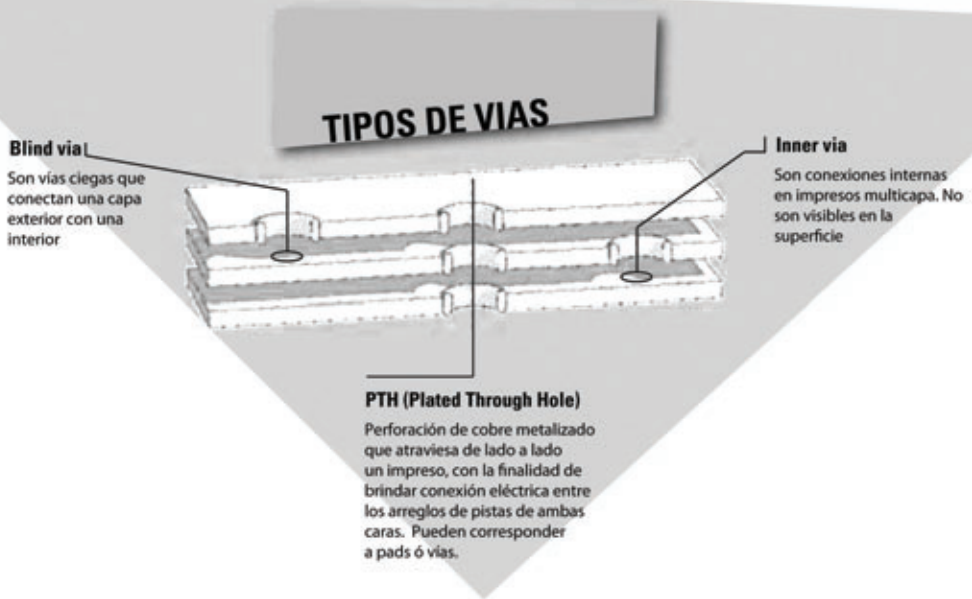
El PCB está formado por una capa de cobre montada sobre un sustrato aislante.
